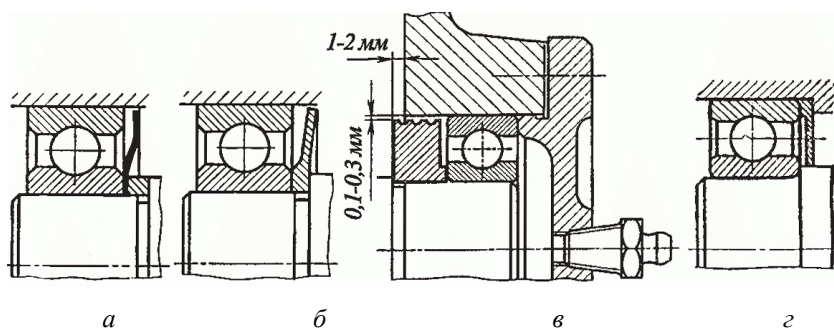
Подшипники с маслоотражательными и мазеудерживающими кольцами
